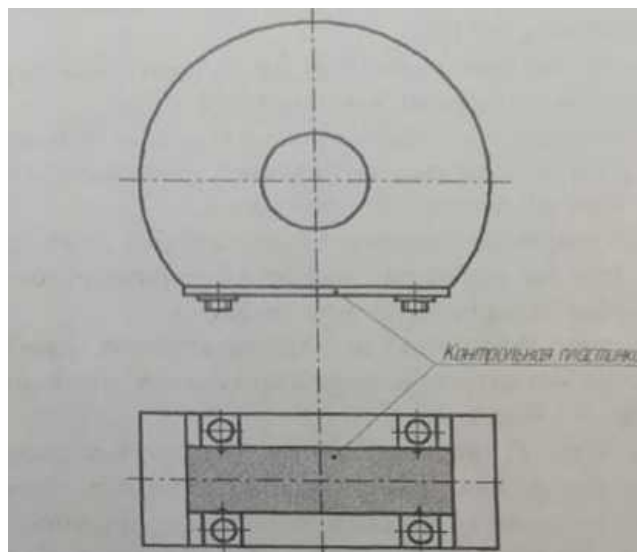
Конструкция приспособления и способ крепления пластин Альмена
